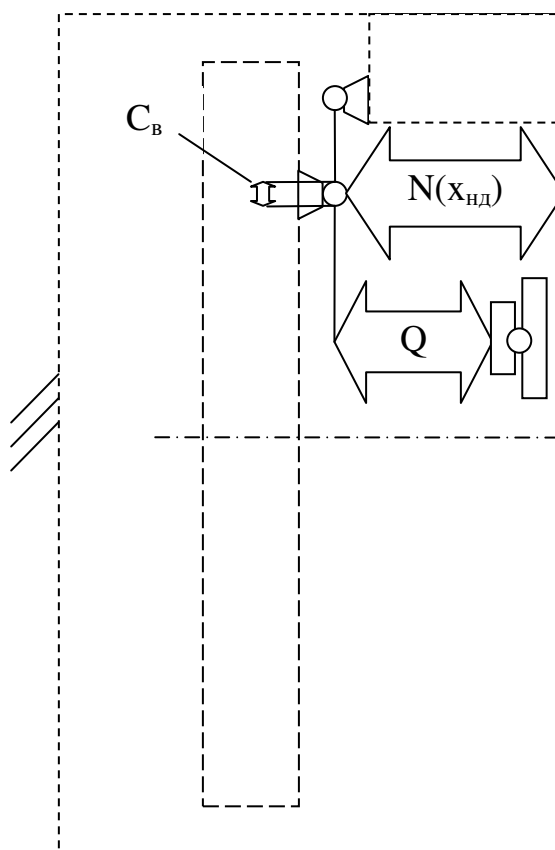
Розрахункова схема діафрагмової пружини
